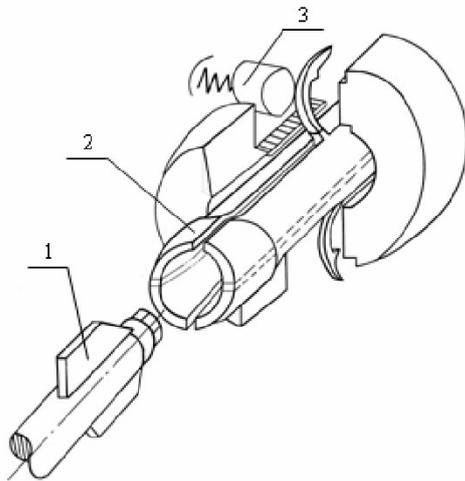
Схема прорезки 4-х пазов на ГKM160: 1 - пуансон; 2 - цанга; 3 - пружинный бойк для отламывания стружки
